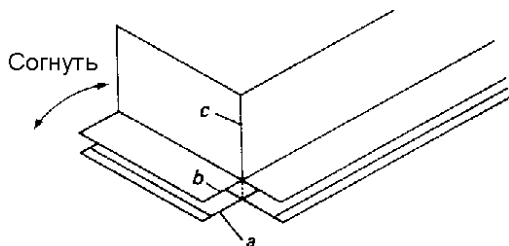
Изгиб и разламывание части держателя (Reynolds Metals Products)
